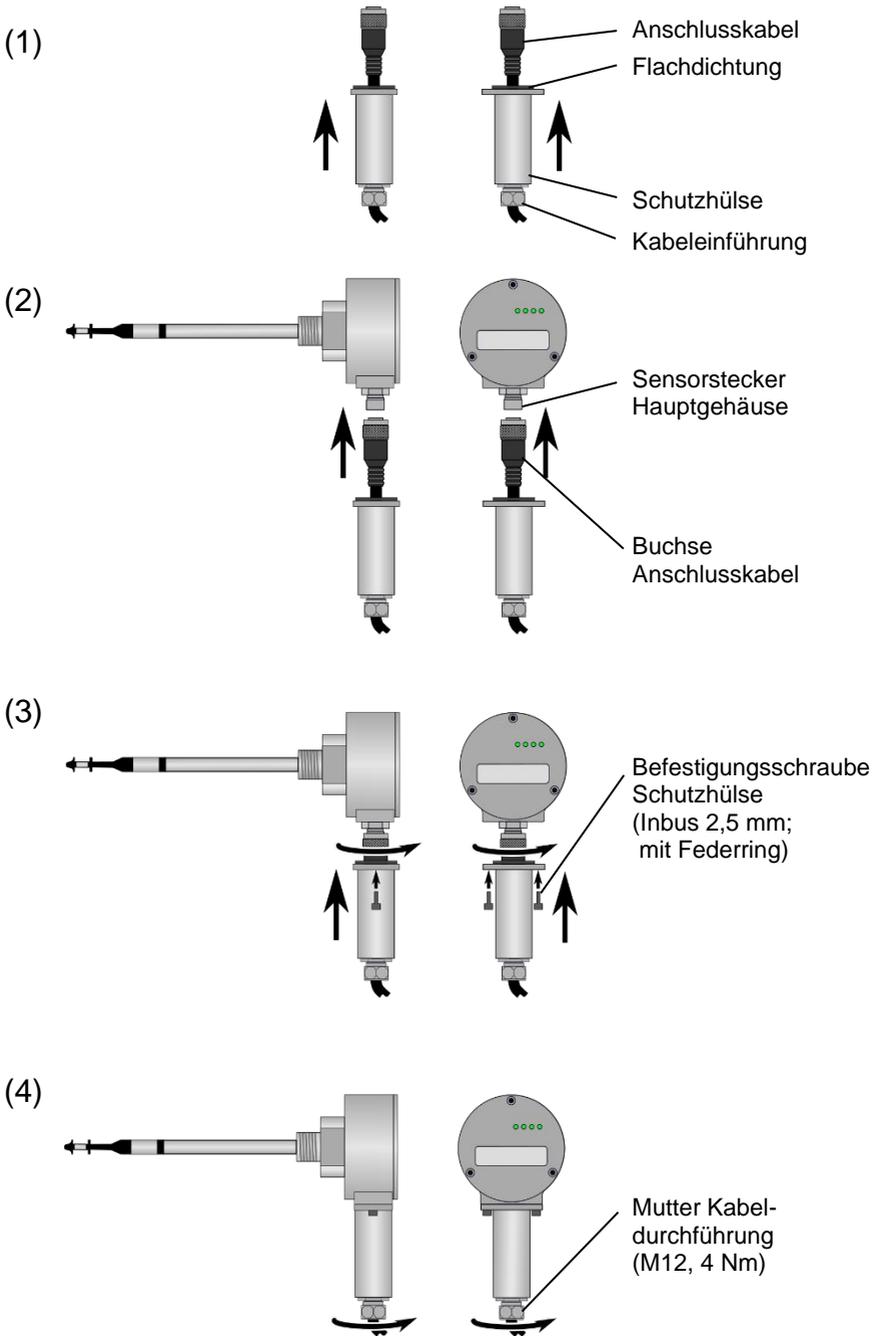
Montage Anschlusskabel mit Schutzhülse
